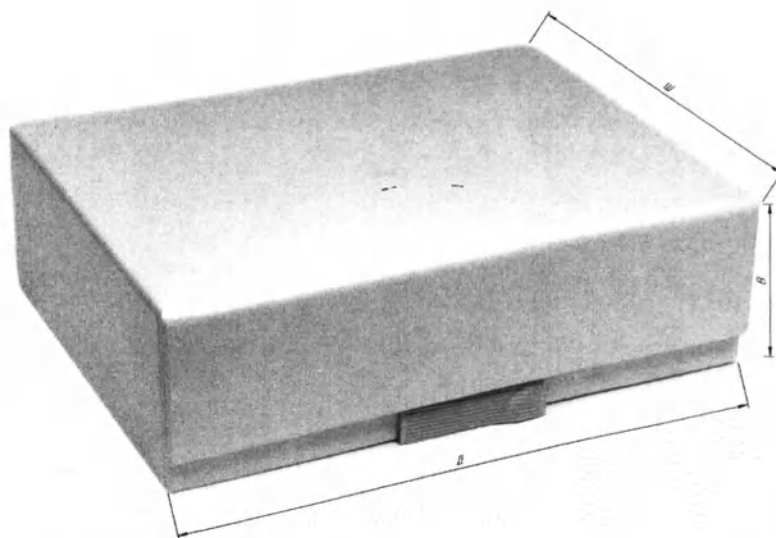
Внешний вид и размеры картонной упаковочной коробки без упаковочного рукава
